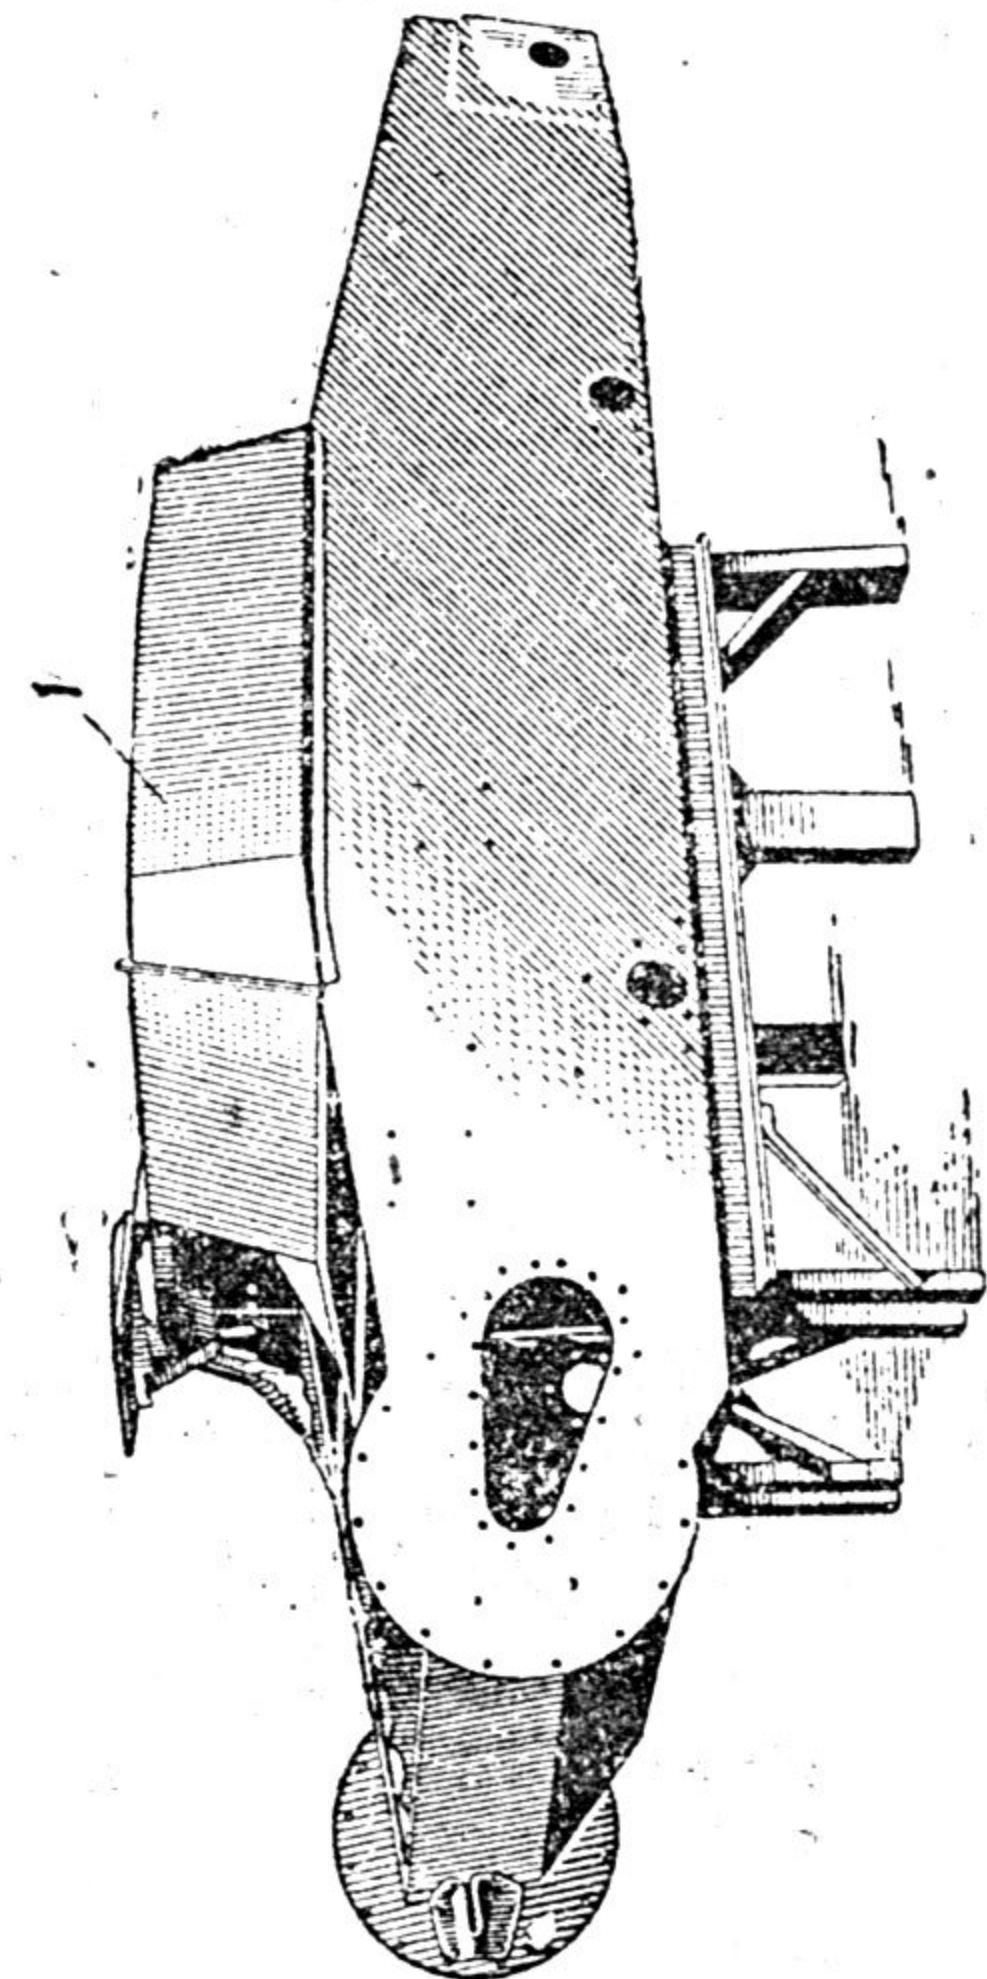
Общий вид корпуса танка с наклонной подбашенной коробкой
